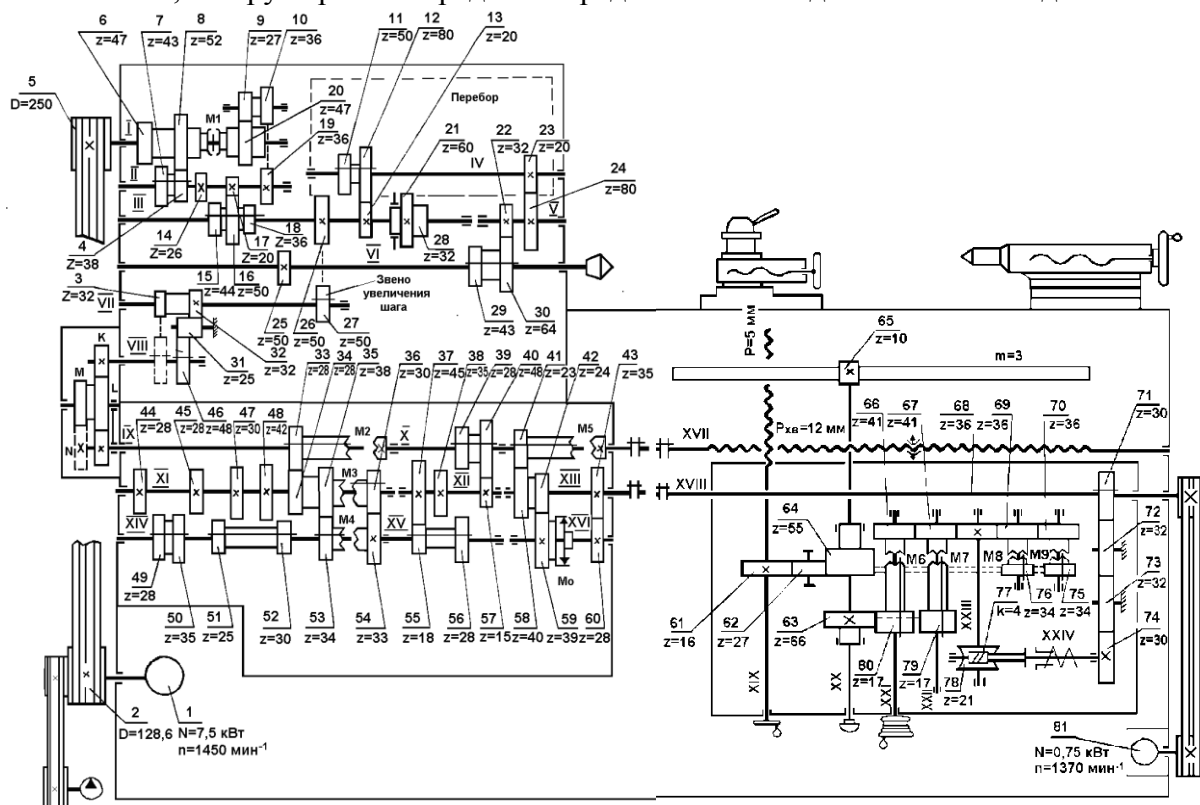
Кинематическая схема токарно-винторезного станка 1B62Г
